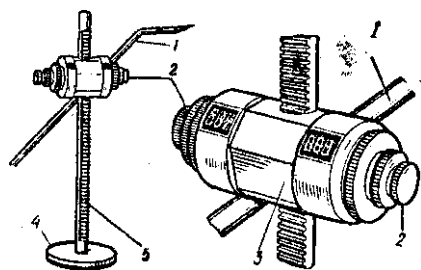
Мікрорейсмус з вимірювальними барабанами
